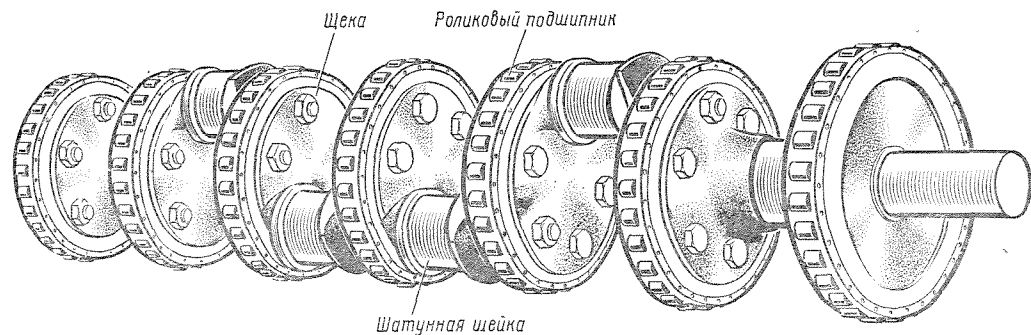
Коленчатый вал с цилиндрическими щеками и роликовыми подшипниками
